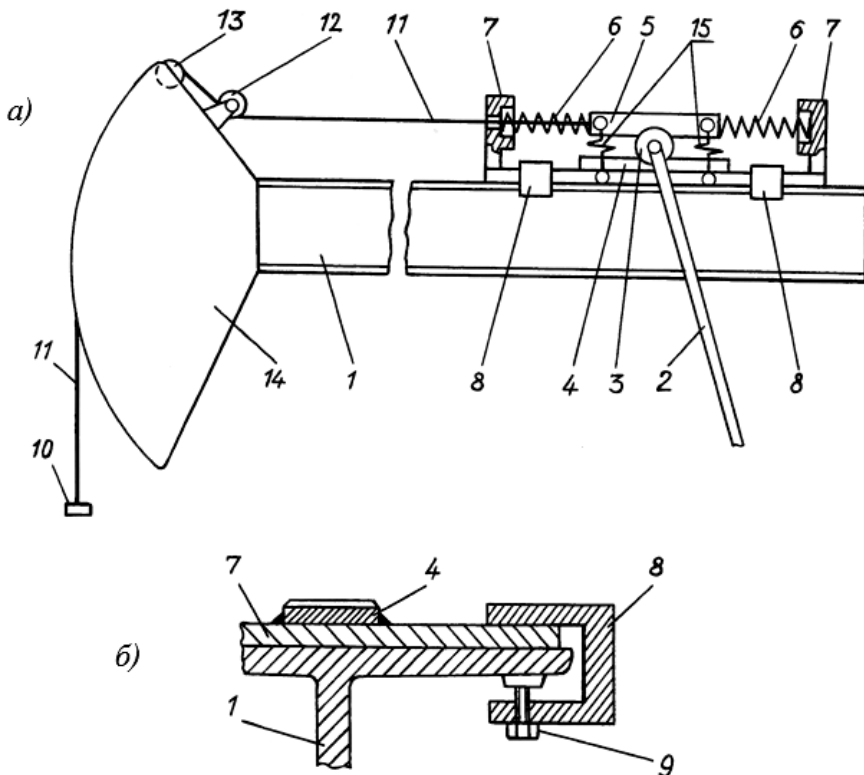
Схема конструкции балансира механизма станка-качалки с устройством для пружинного уравнивания: а) общий вид; б) приспособление для крепления опоры на балансире
